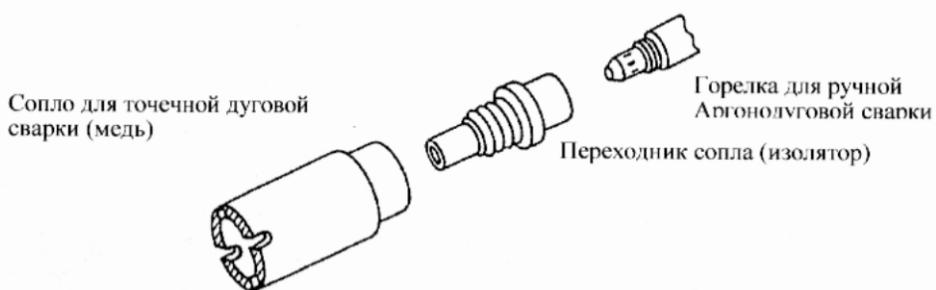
Оснастки для точечной дуговой сварки
